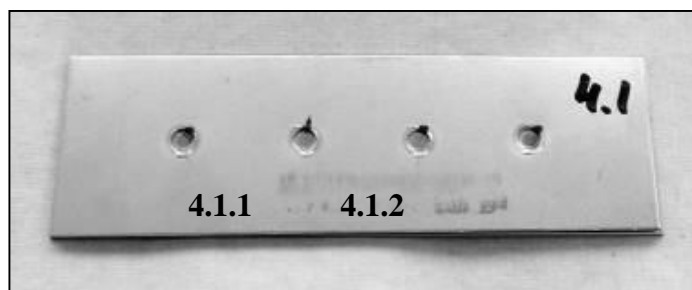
Внешний вид точечной контактной сварки образца № 4.1
